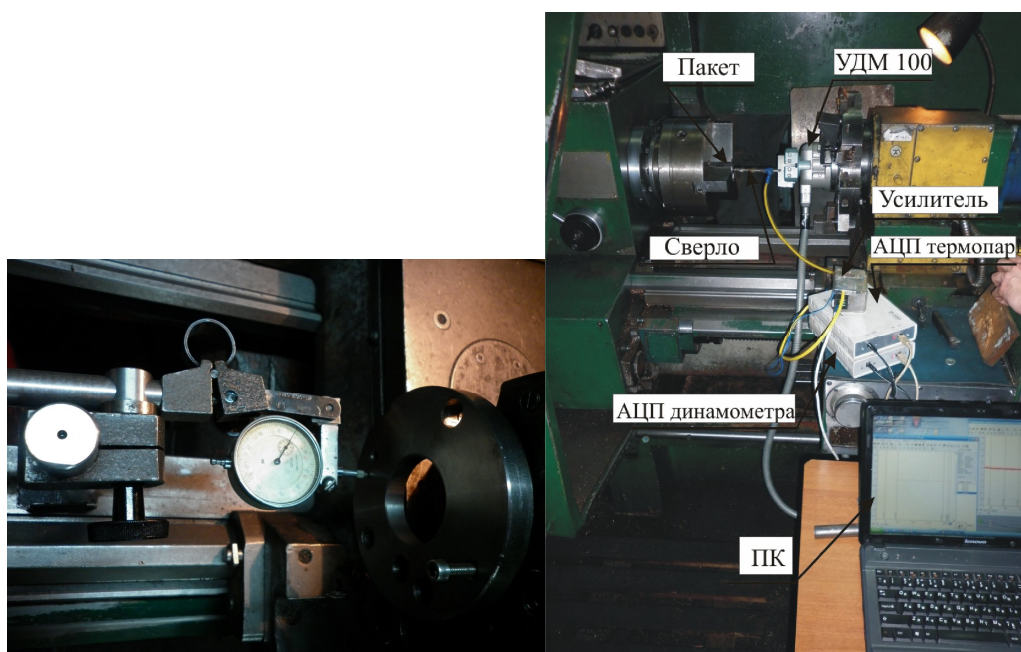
Схема наладки токарного станка 16Б16Т1
